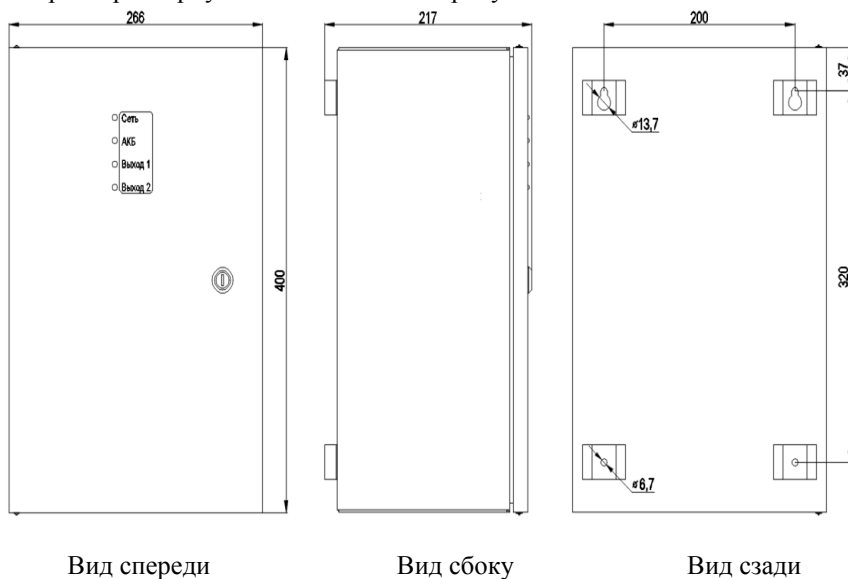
Внешний вид, габаритные и установочные размеры корпуса ББП
